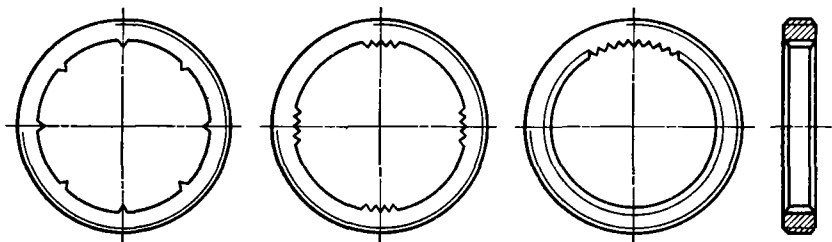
Кольцевые гайки с наружной резьбой, треугольными шлицами и выступами
